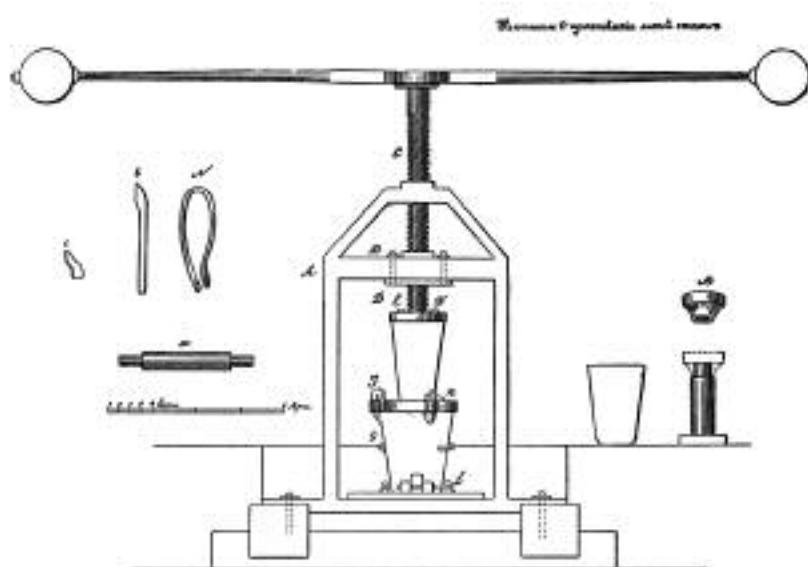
Схема устройства пресса и приспособления, применяющиеся при изготовлении тиглей
